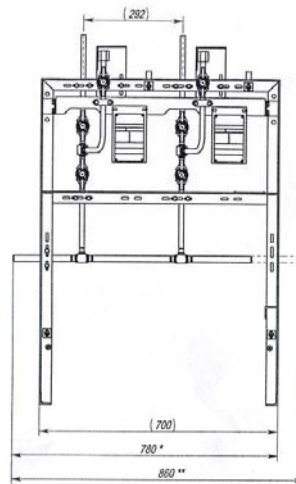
Панель для установки приборов штуцерной конструкции двухместная
